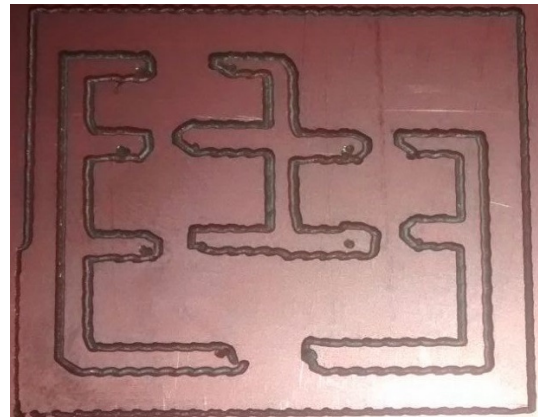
Parte 1 - Circuito impreso realizado por la máquina fresadora
